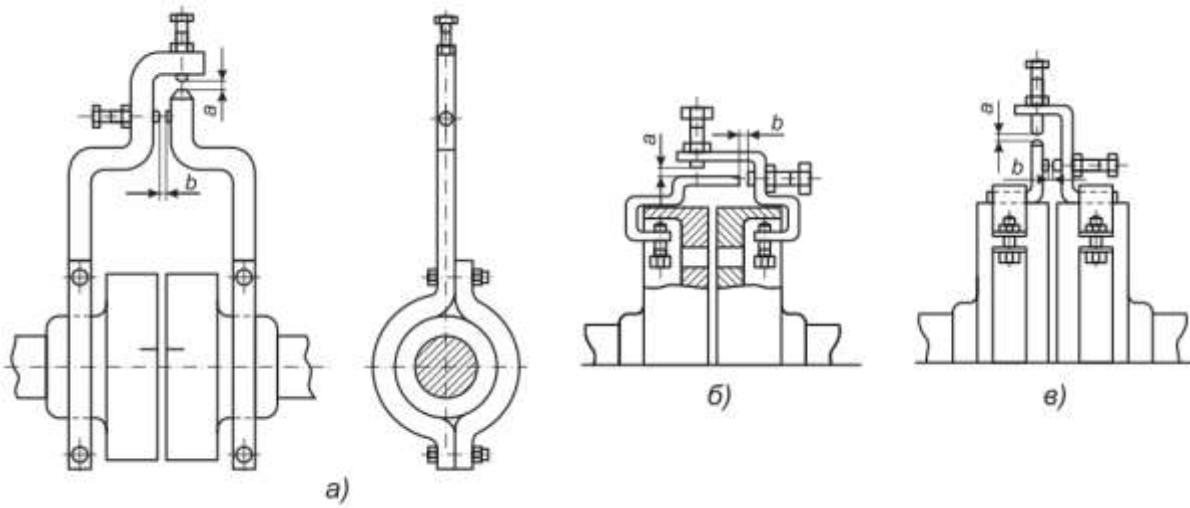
Скобы для центровки полумуфт: *a* — центровочные скобы; *б* — центровочные приспособления; *в* — центровочные приспособления с хомутами
